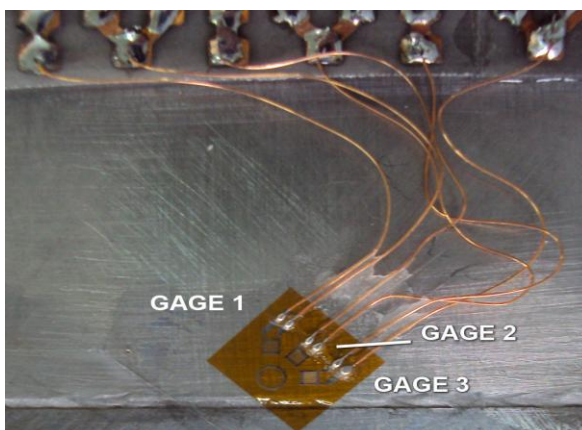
Colagem do extensômetro: gage 1 na direção x (perpendicular ao cordão de solda)
